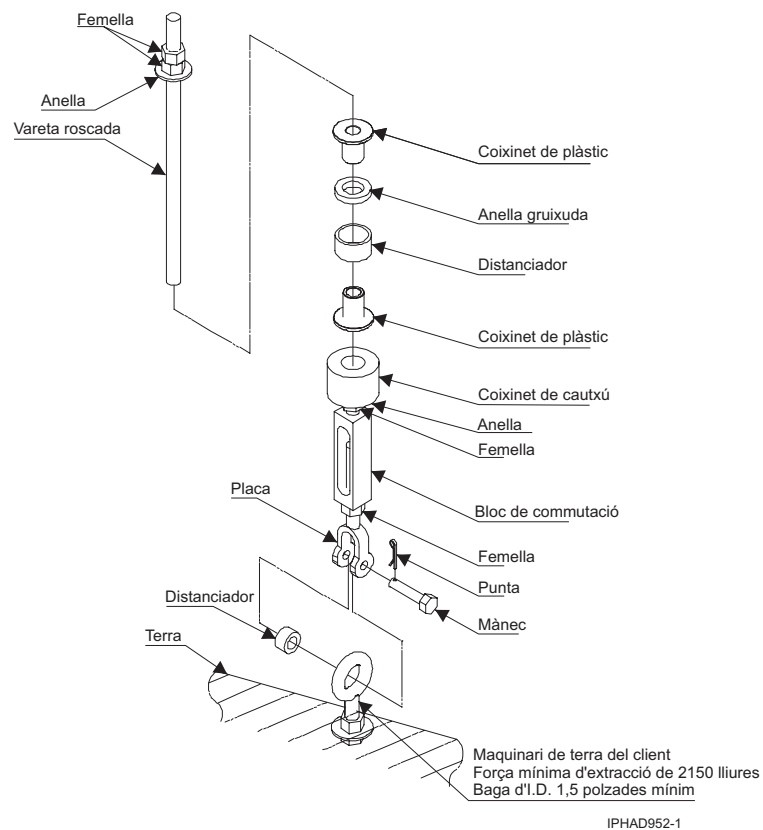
Maquinari de fixació del bastidor al conjunt del cargol tensor per a una tarima de 228,6 - 330,2 mm (9 - 13 polzades) (número de peça 44P2999)
